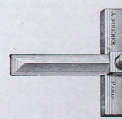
Équerre à T forte, en acier, à branche mobile. . 18 fr.
